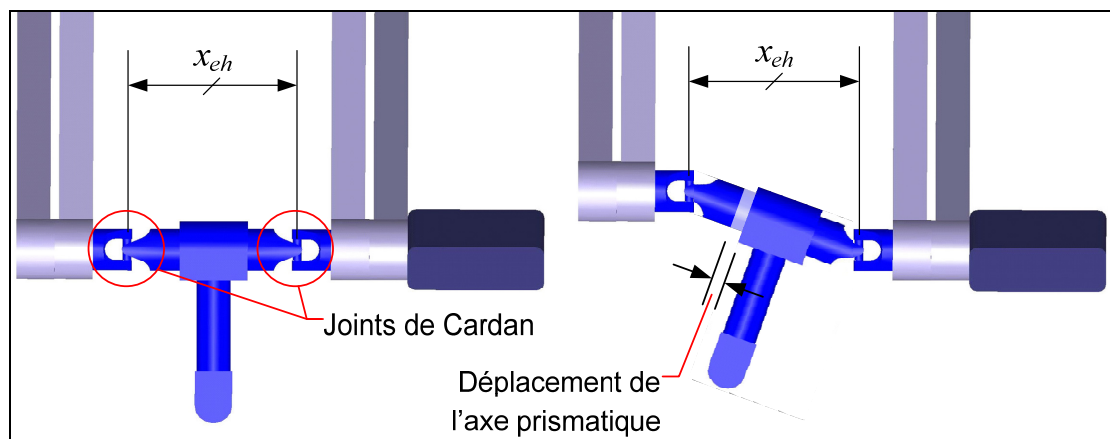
Mécanisme de l'axe prismatique et positionnement des joints de Cardan
